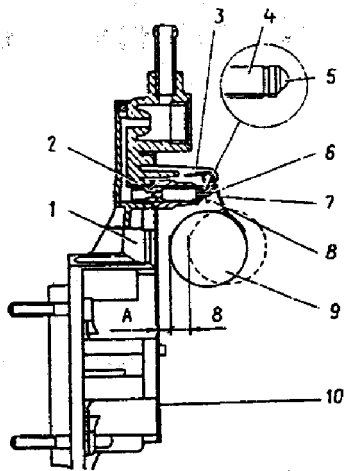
Verificação da altura da bóia: 1 - tampa do carburador; 2 - assento da válvula de agulha; 3 - limitador; 4 - válvula de agulha; 5 - esfera da agulha de vedação; 6 - garrilha posicionador da agulha da válvula; 7 - suporte da bóia; 8 - lingueta; 9 - bóia; 10 - junta.
